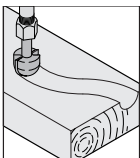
Beim Fräsen die Oberfräse tangential zur Werkstückkante mitschwenken, um gleichmäßige Fräskanten zu erzielen.
